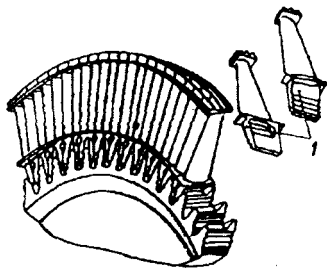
Рабочие лопатки турбины двигателя ЛД-25 со сдвоенными разрезными замками:
